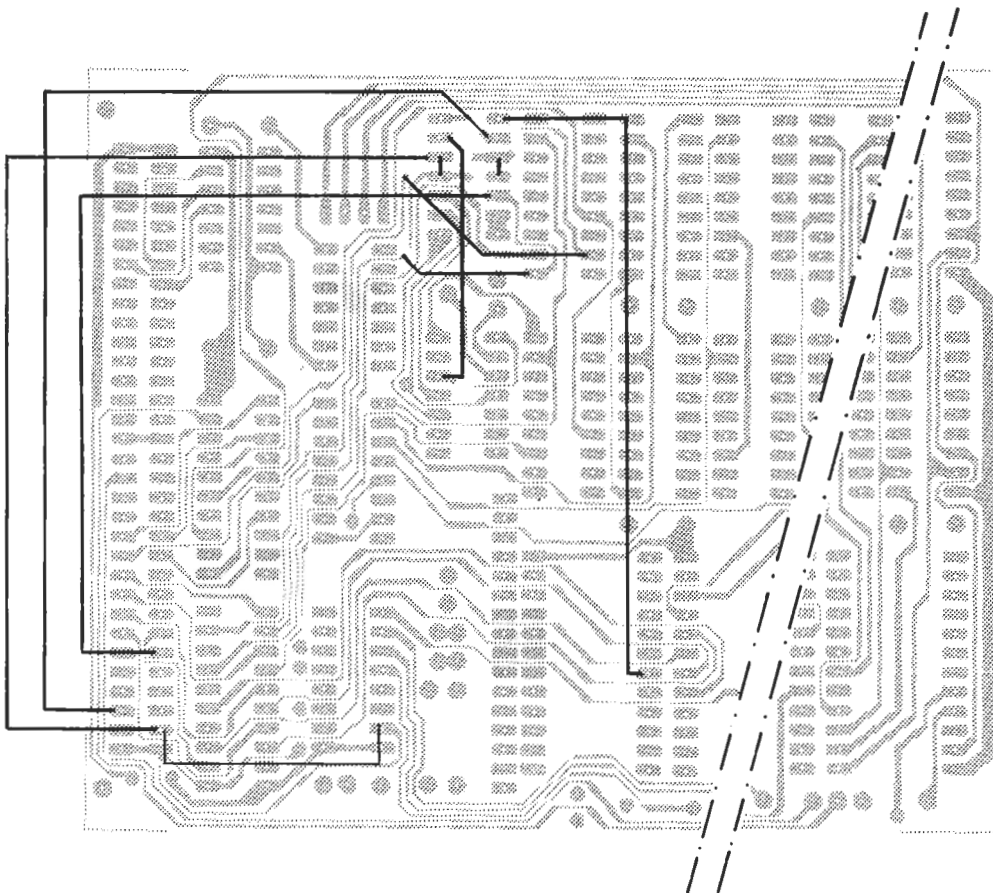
Nuevos puentes a colocar en el lado de soldadura de la placa de circuito impreso.
